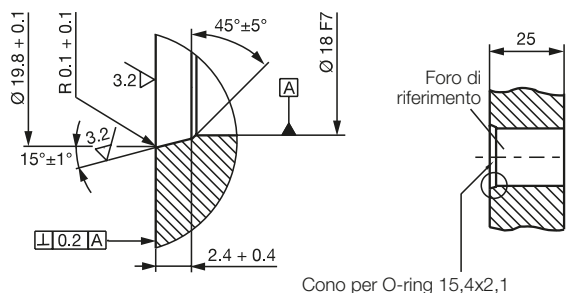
Foro di riferimento per il montaggio del BTL con l'O-ring
